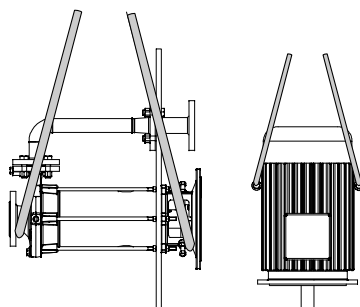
Transportera pump och motor separat från motorstorlek 180 för stora monteringsdjup
